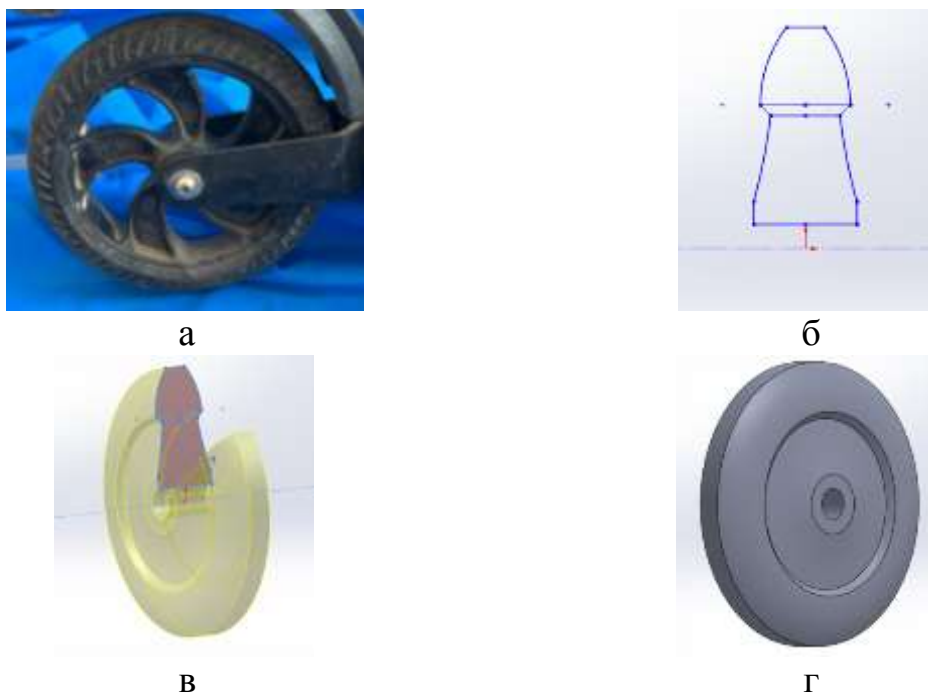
Ведомое колесо; а – реальный вид; б – эскиз ведомого колеса; в – команда «повернуть» эскиз; г – 3D-модель
